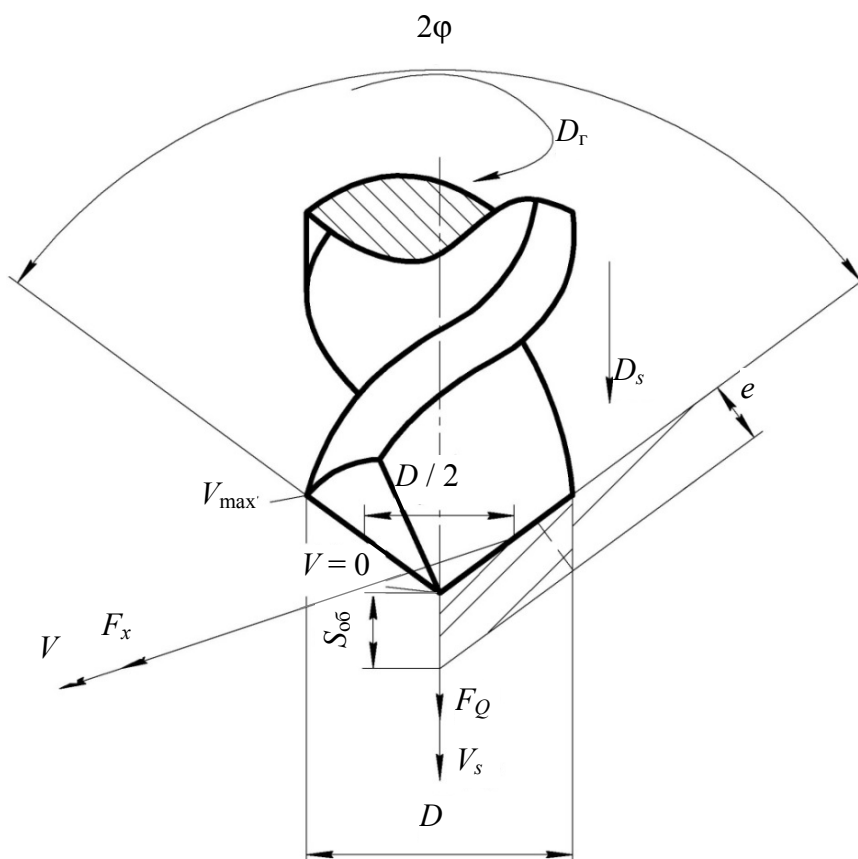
Схема сил и направления движений сверла спирального с конической заточкой с углом при вершине 2φ
